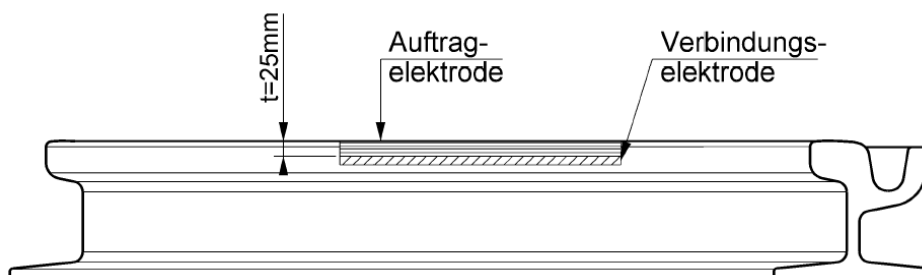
Reparaturschweißen mit Stabelektrode
